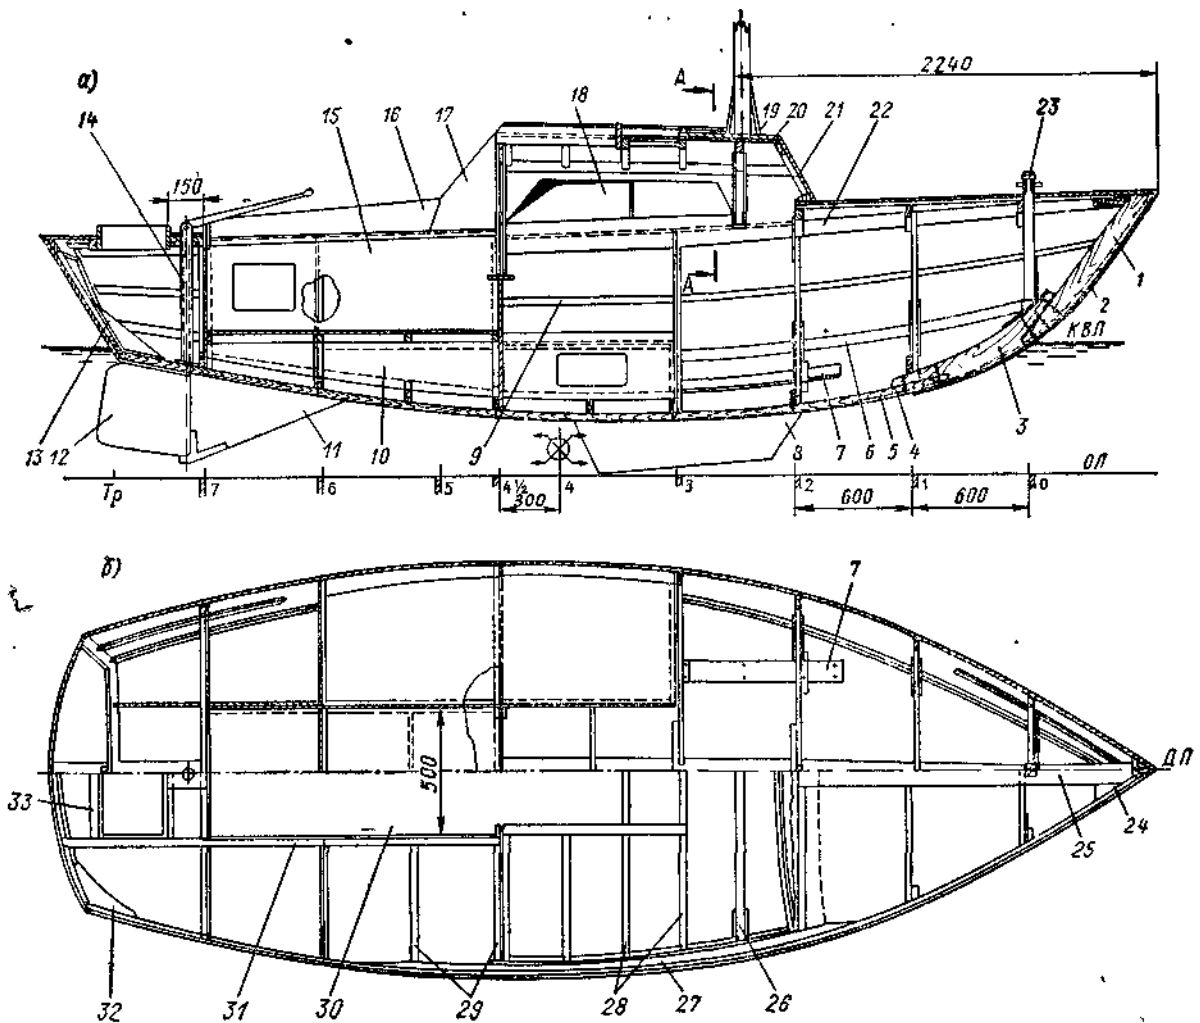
Конструктивный чертеж корпуса: а — продольный разрез; б — вид со снятой палубой и набор палубы.
